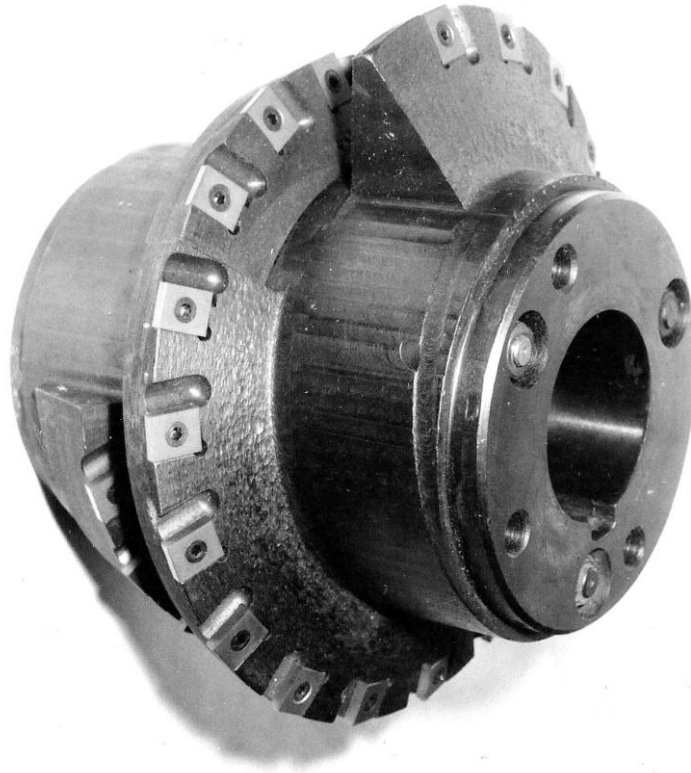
Правый корпус фрезы одностороннего резания $m=20$ мм, состоящий из 2-х одновитковых корпусов
